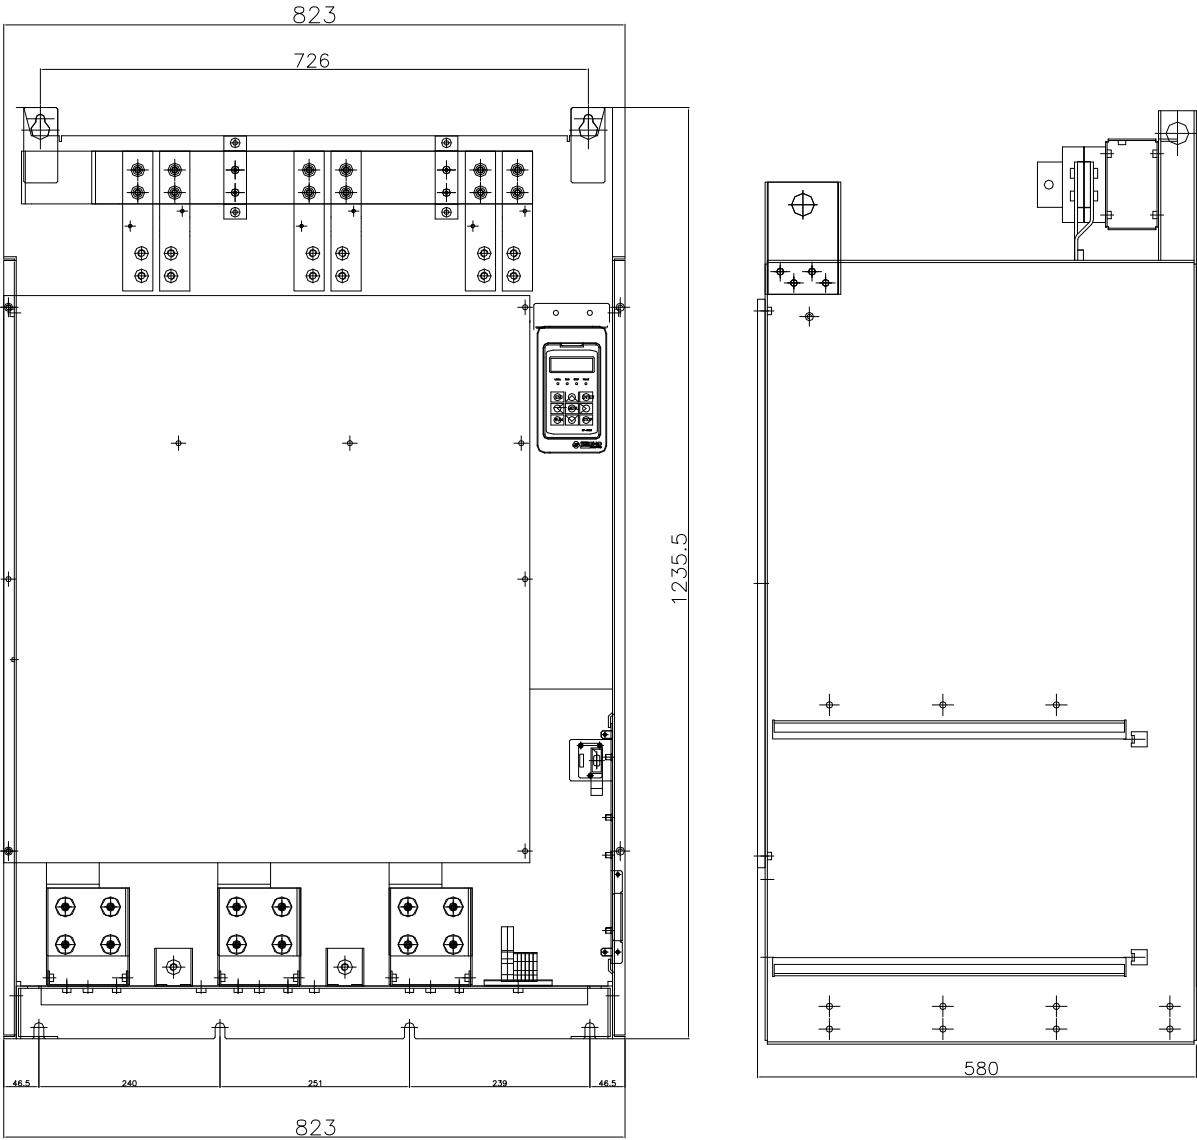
(1) K10B INVERTER UNIT 外壳外形尺寸
